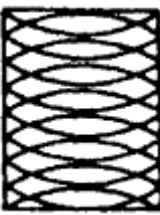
Общий вид образцов шероховатости,поставляемых отдельными образцами
